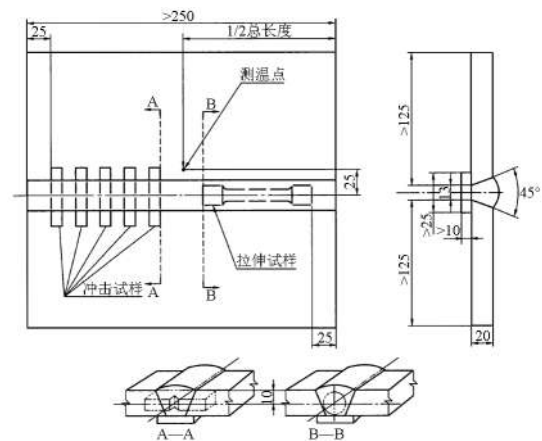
焊接后力学性能试验的试件制备(单位:mm)
